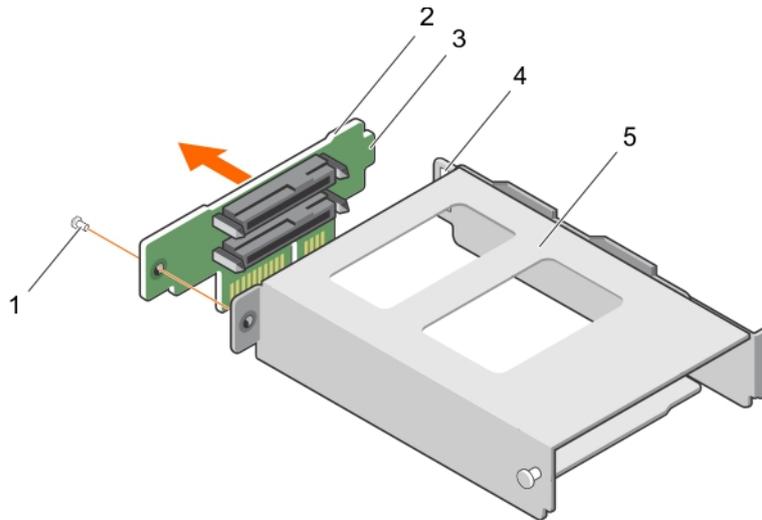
Extracción del plano posterior de la SSD de 1,8 pulgadas
